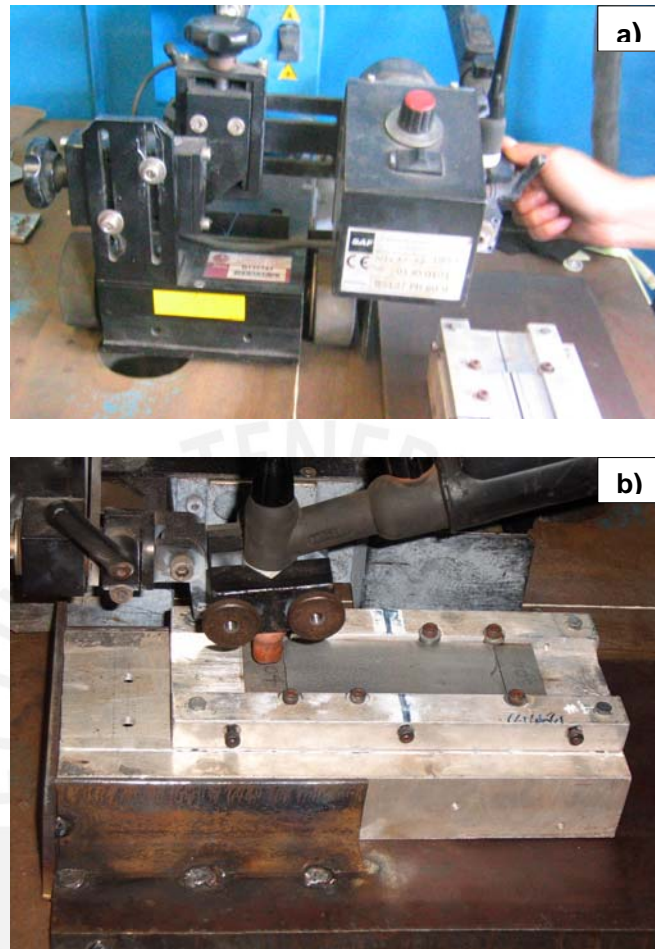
a) Posicionamiento del carro de avance antes del soldeo
